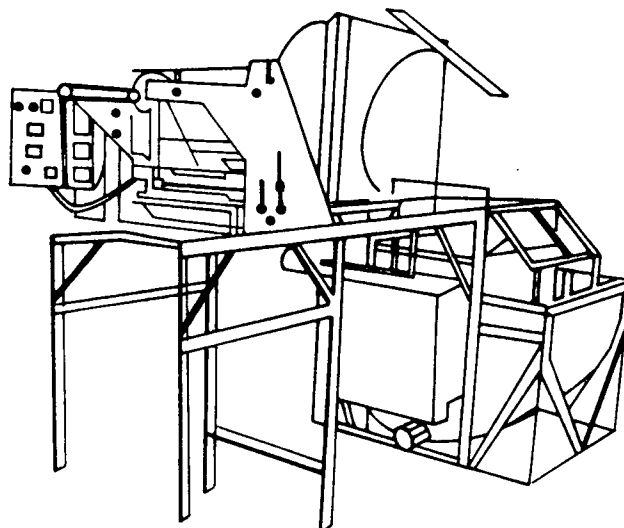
Montagem da máquina desoperculadora e extratora [8].
